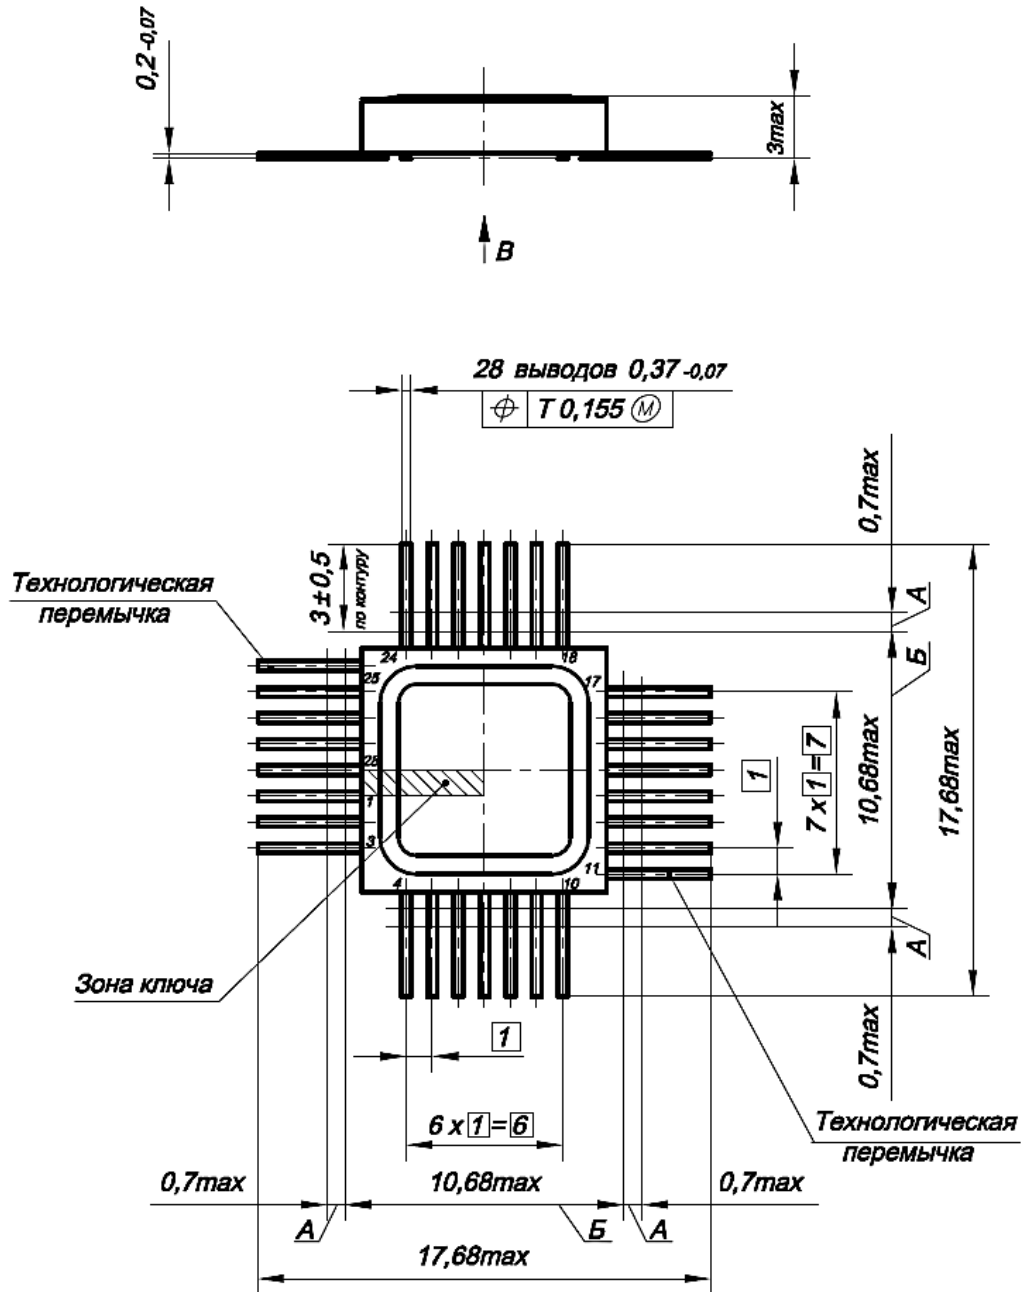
Габаритный чертеж корпуса Н09.28-1В
